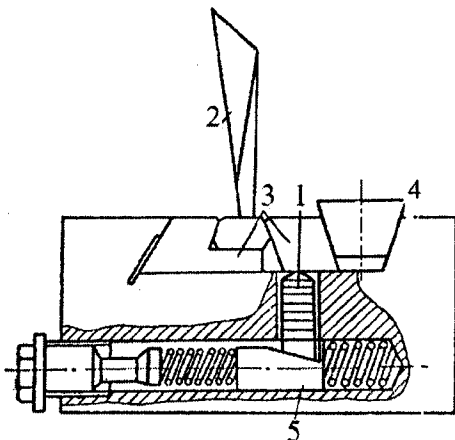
Схема универсального устройства для крепления и возбуждения колебаний лопаток компрессора и турбины: 1 – набор пьезокерамических пластин; 2 – лопатка; 3 – сменные вкладыши для зажима лопаток; 4 – стяжной клин; 5 – подвижный клин
